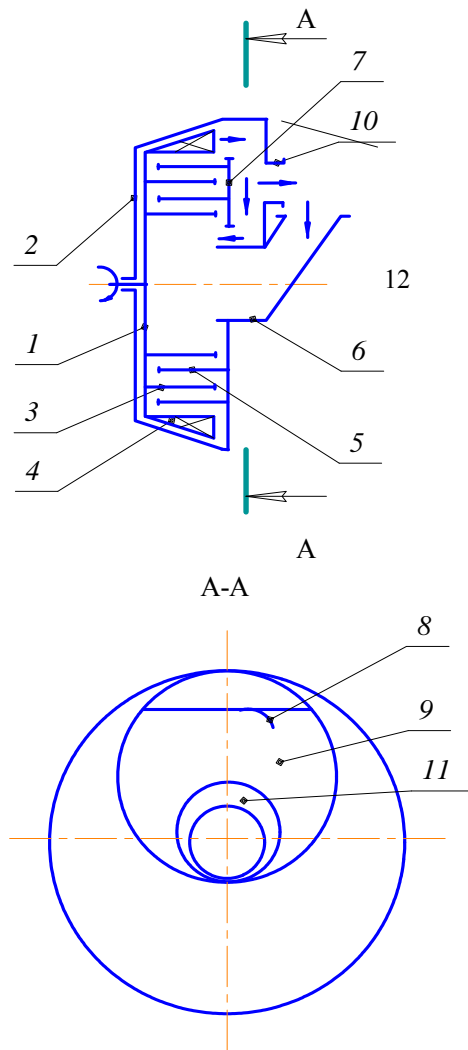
Дисмембратор с классифицирующей камерой: 1 – ротор; 2 – корпус; 3, 5 – измельчающие элементы; 4 – крыльчатка; 6 – крышка; 7 – стенка; 8, 11 – отверстия; 9 – классифицирующая камера; 10 – выгрузочный патрубок; 12 – загрузочный патрубок
